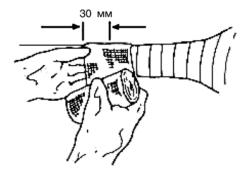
Обмотка корпуса лентой «Арморкаст».
